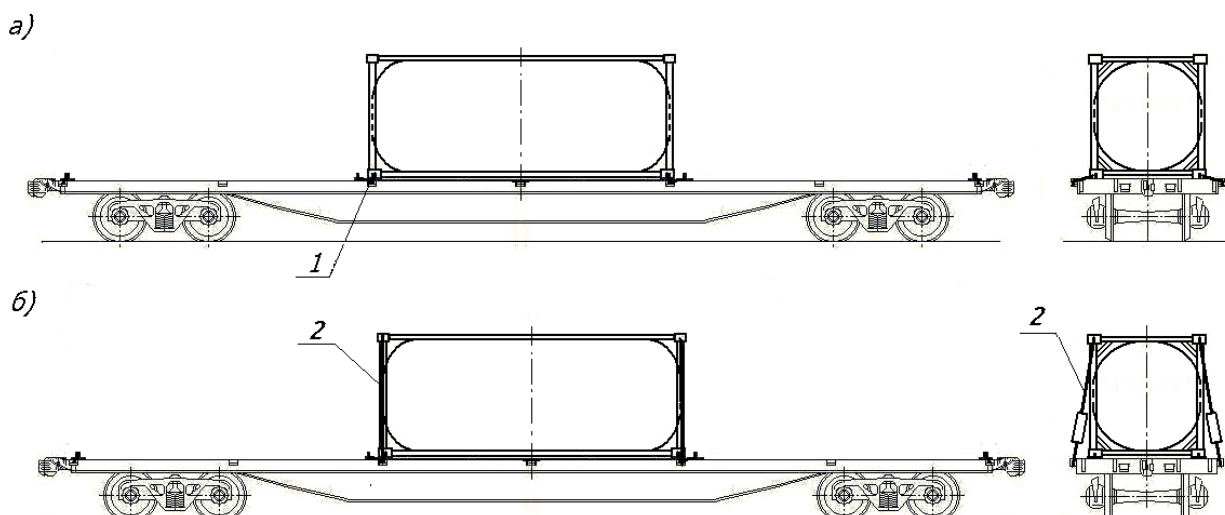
Дополнительное крепление контейнера-цистерны на платформе для крупнотоннажных контейнеров:
